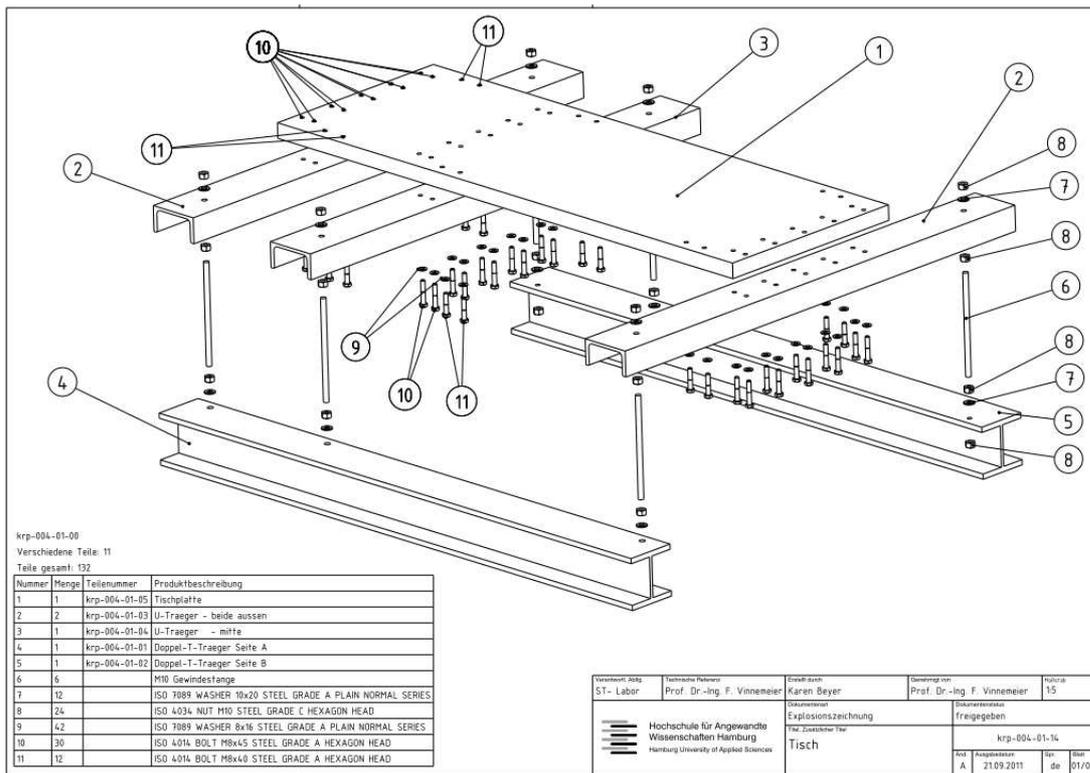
Baugruppe: Tisch - Technische Explosionszeichnung mit Stückliste - *krp-004-01-14
